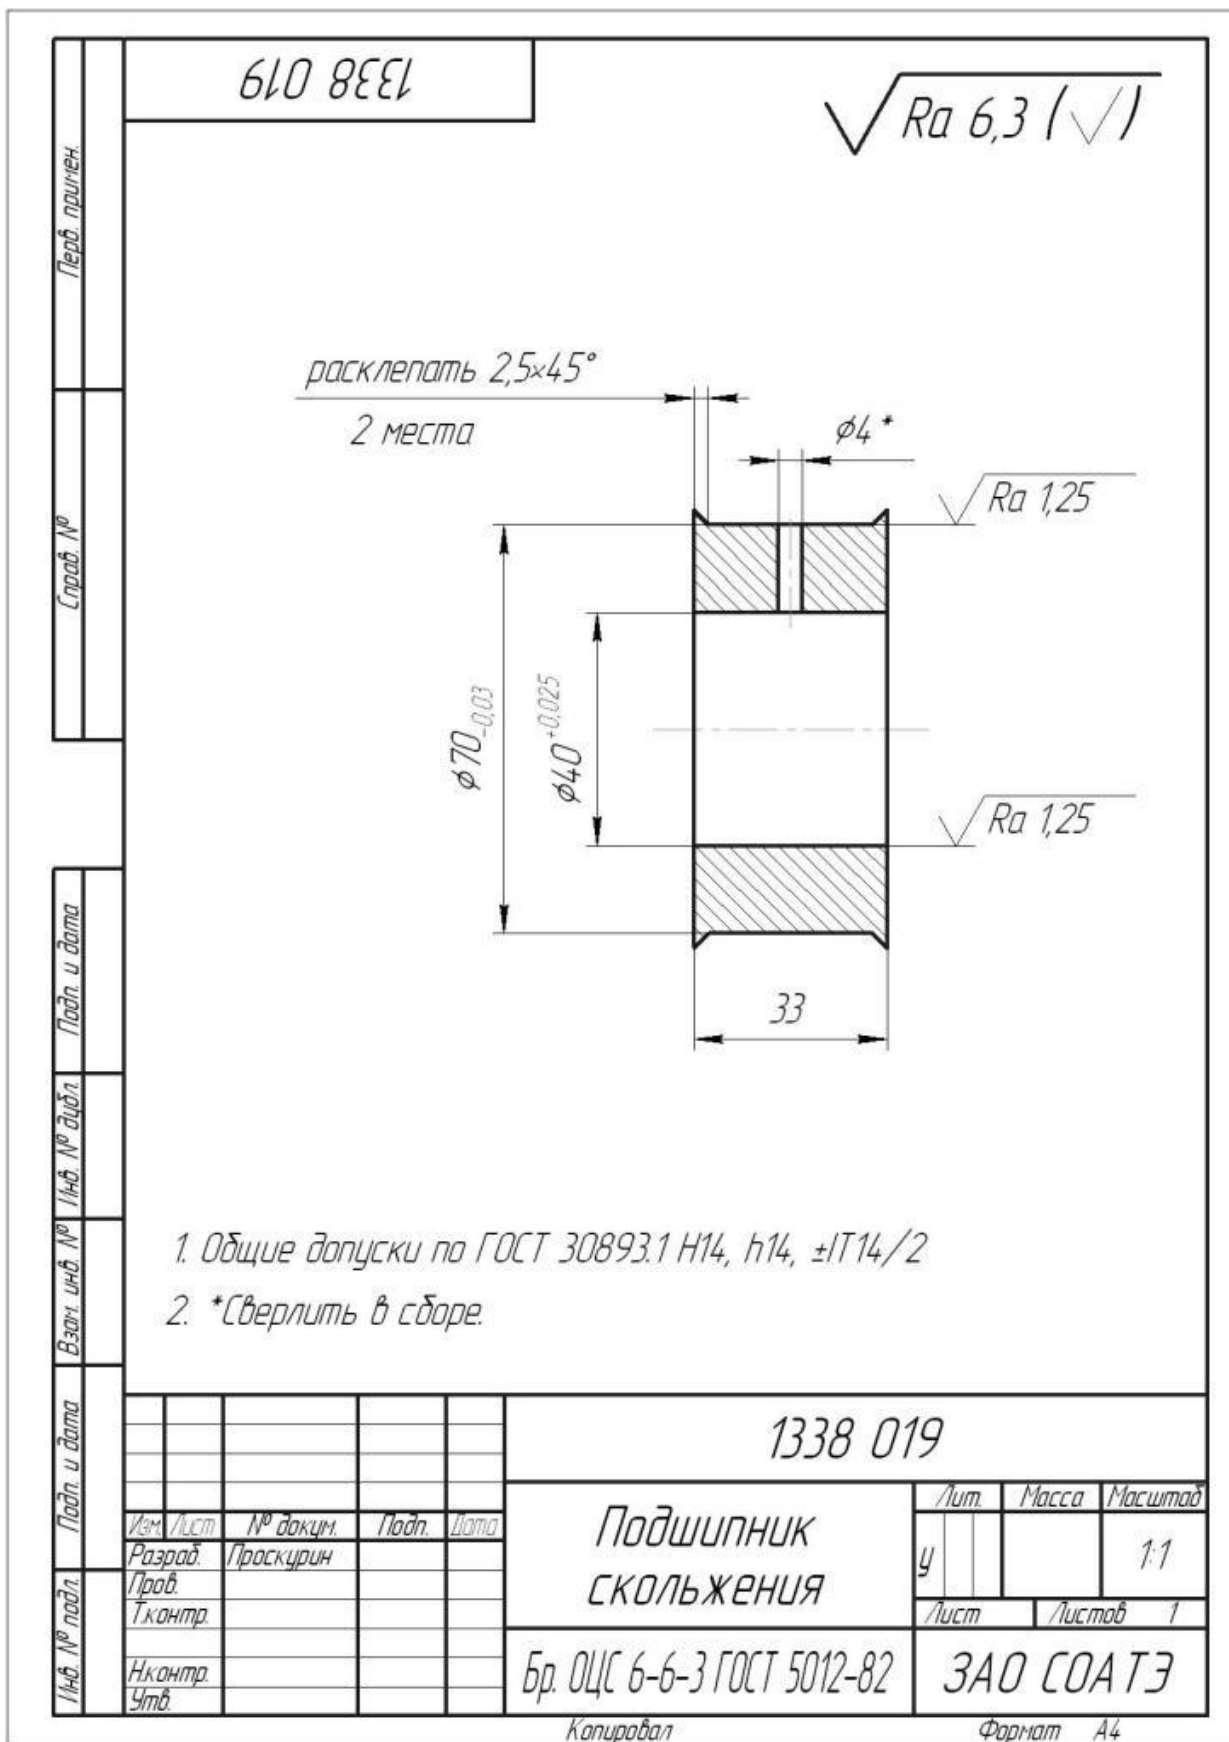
Деталь испытательного стенда. Подшипник скольжения
